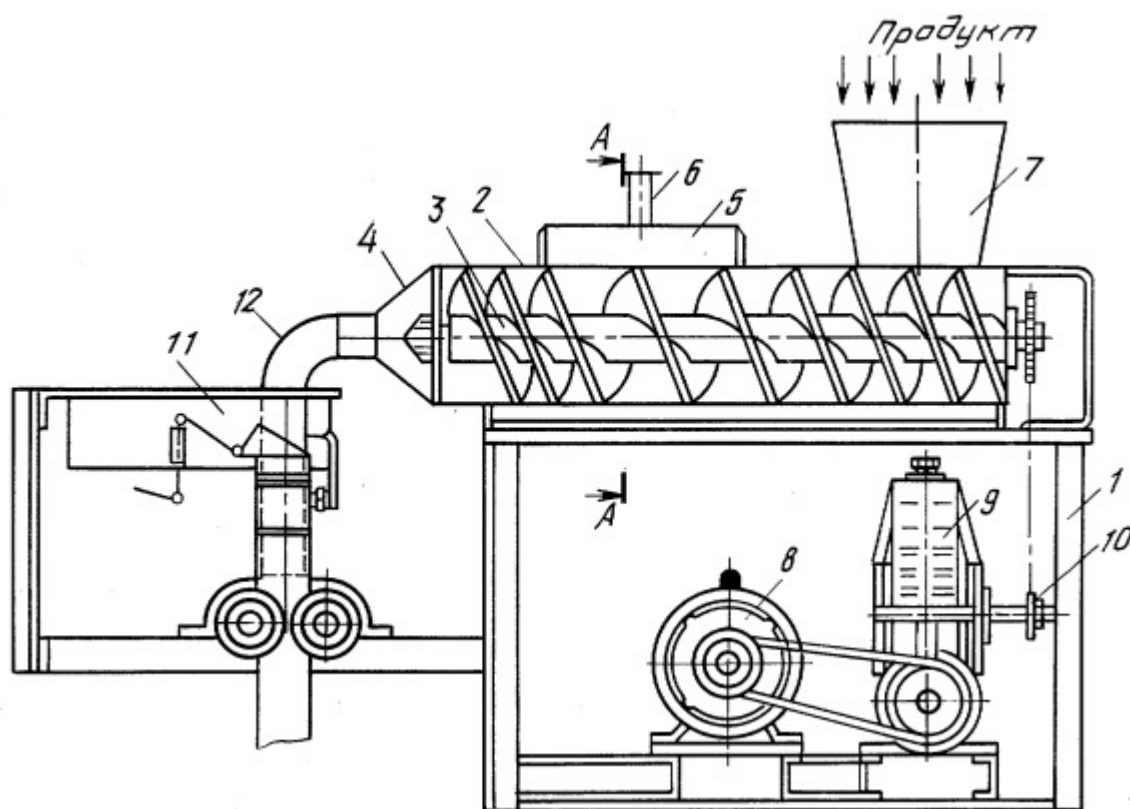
установка для охлаждения творога (А.С. №1355190)
